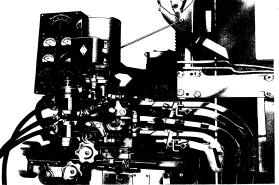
Механизм подачи электродных проволок и токоподвод ящие мундштуки аппарата А-372 Fig. 7. A-372 Welding Apparatus electrode wire feeding mechanism and current-leading electrode holders
